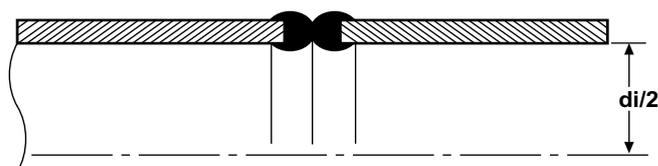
Soldadura a tope con herramienta caliente
